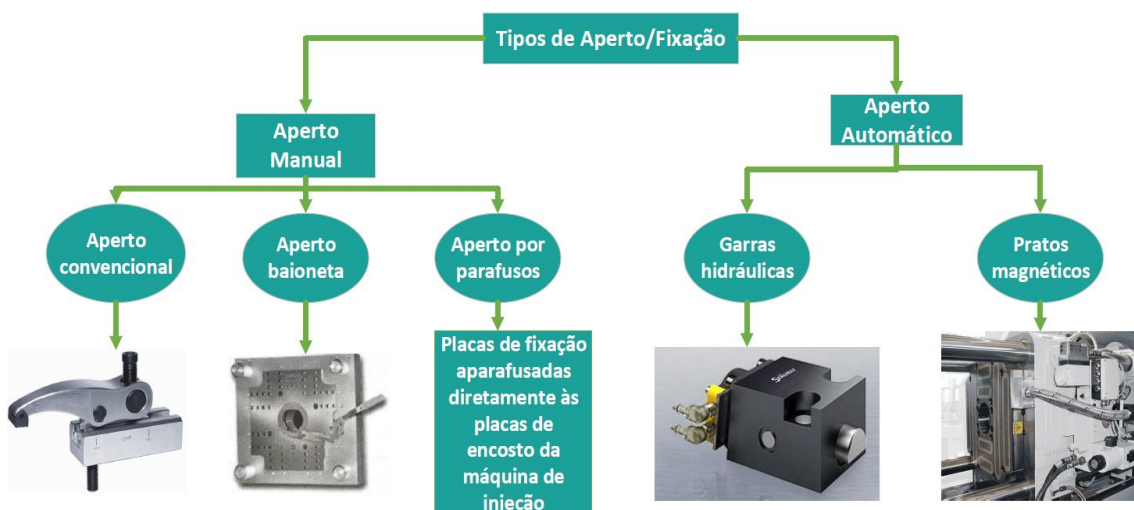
Tipos de fixação do molde à máquina de injeção [1,17,18]
